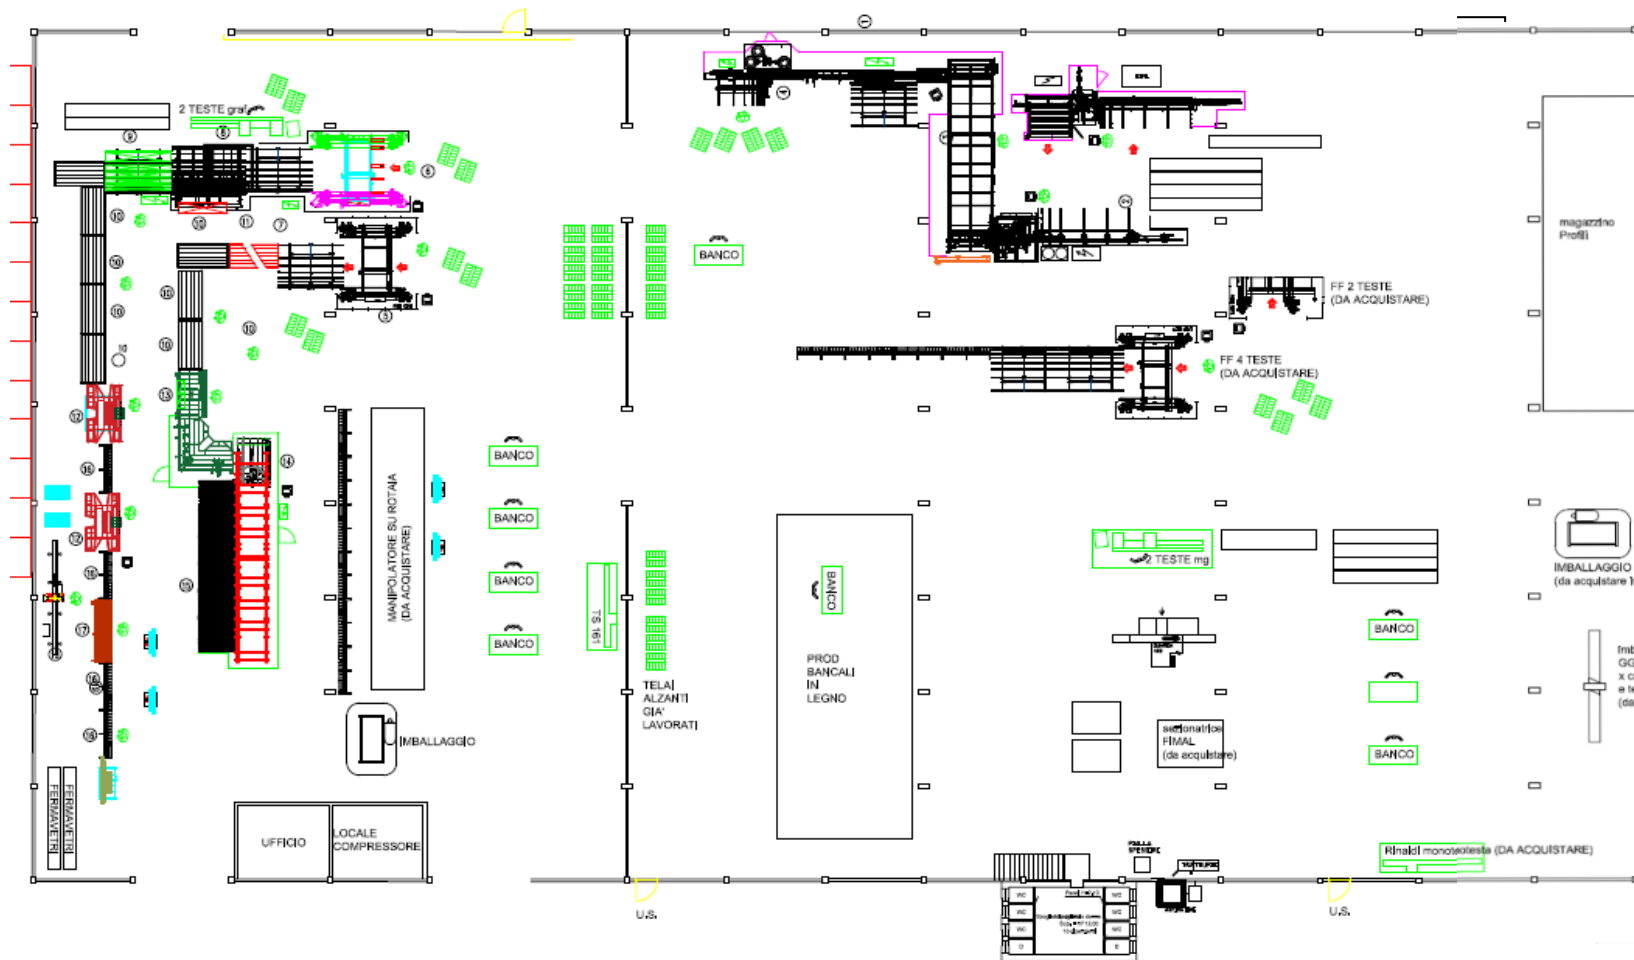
Planimetria generale dell'unità 2 in progetto;
